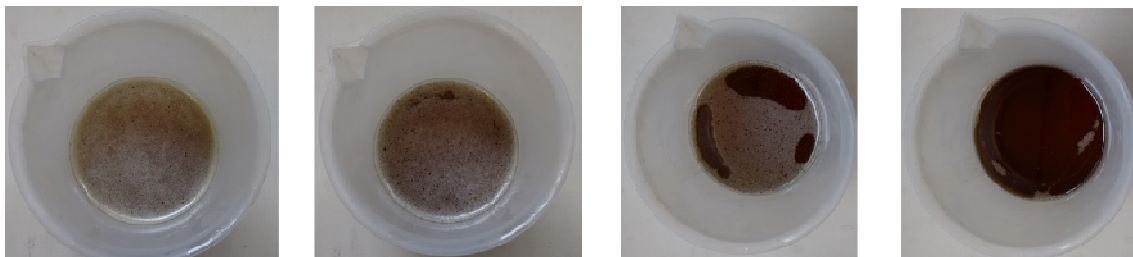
Eliminação das bolhas da resina antes da moldagem
